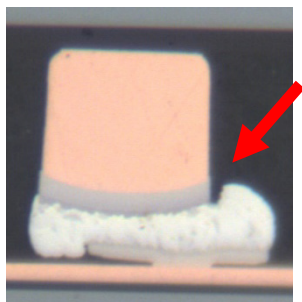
Interconnexion à soudure non montante pour Flux 2(gauche)
